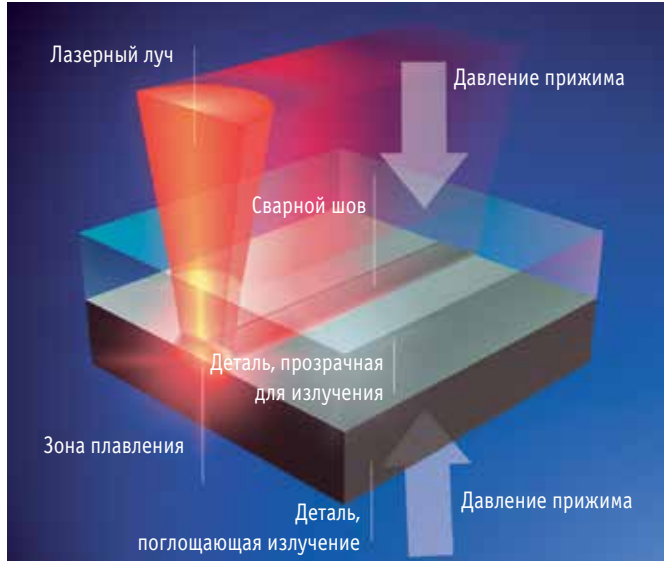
Схема лазерной сварки полимерных материалов просвечиванием
